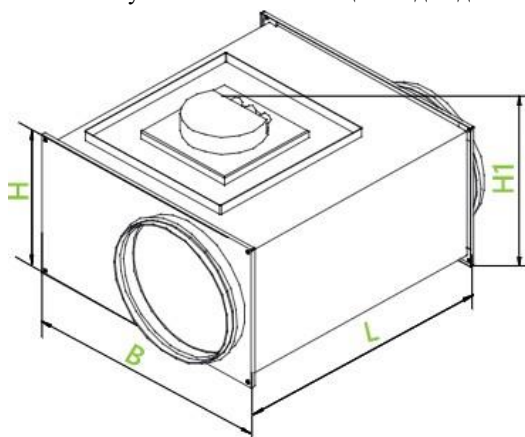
Габаритные установочные и присоединительные размеры вентиляторов
